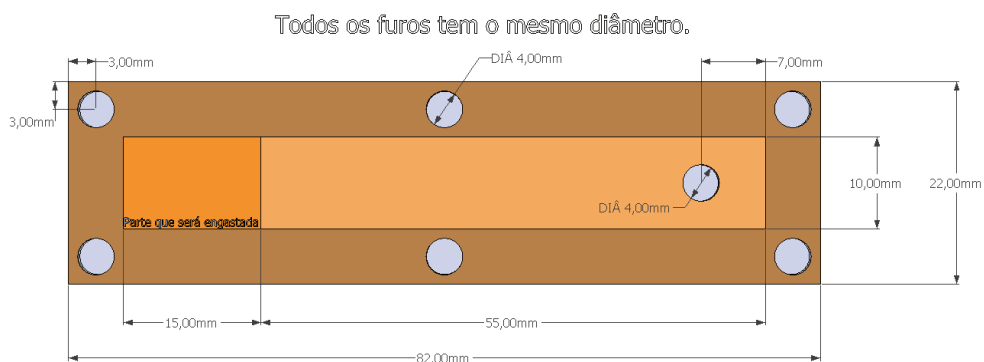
Vista superior da chapa de latão que foi usinada em fresa CNC.
